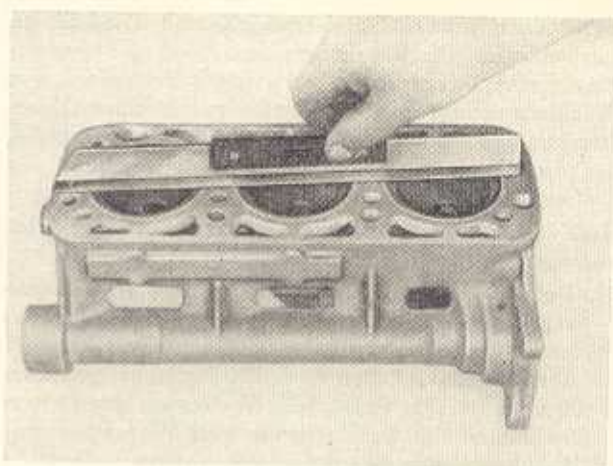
Überprüfen der Planfläche mit Haarlineal
